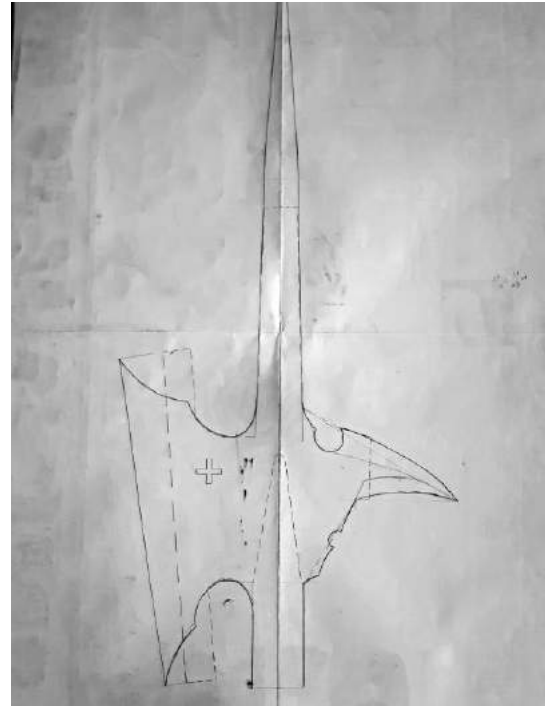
Werkstattplan, gestrichelte Linie markiert den Rohling des Körpers
